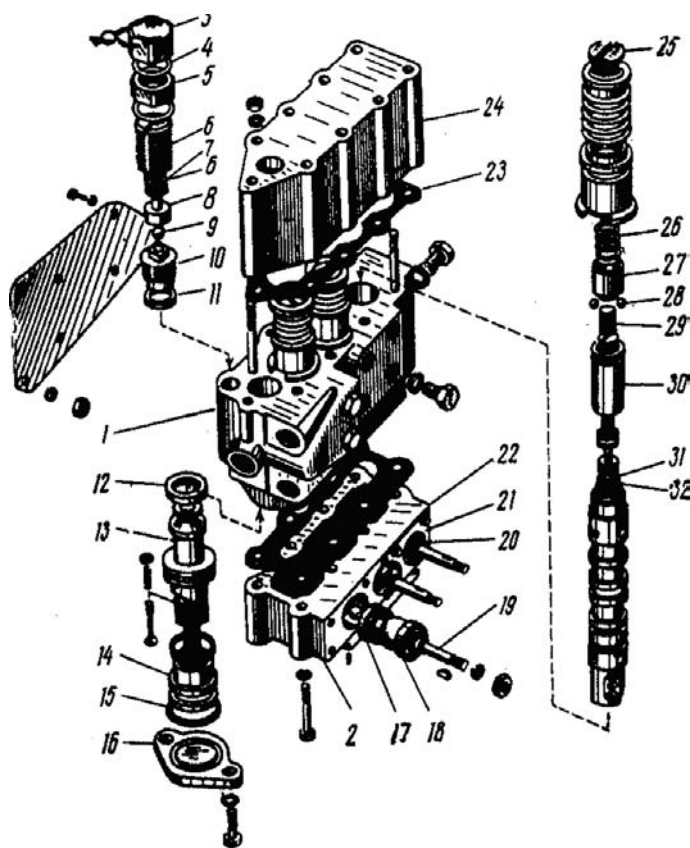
Разборка распределителя. 1 — корпус распределителя; 2 — верхняя крышка; 3 — колпачок; 4 — уплотнительное кольцо; 5 — гайка; 6 — рег. улировочный винт; 7 — пружина предохранительного клапана; 8 — направляющая предохранительного клапана; 9 — предохранительный клапан; 10 — гнездо предохранительного клапана; 11 — уплотнительная шайба; 12 — гнездо клапана; 13 — перепускной клапан; 14 — направляющая клапана; 15 — кольцо; 16 — упор; 17 — нижнее кольцо; 18 — верхнее кольцо; 19 — рычаг; 20 — г. офрированный пыльник; 21 — пластина пыльника; 22 — пластина колец; 23 — нижняя прокладка; 24 — нижняя крышка; 25 — пробка золотника; 26 — пружина фиксатора; 27 — втулка фиксатора; 28 — фиксатор; 29 — бустер; 30 — гильза золотника; 31 — прокладка; 32 — фильтр
